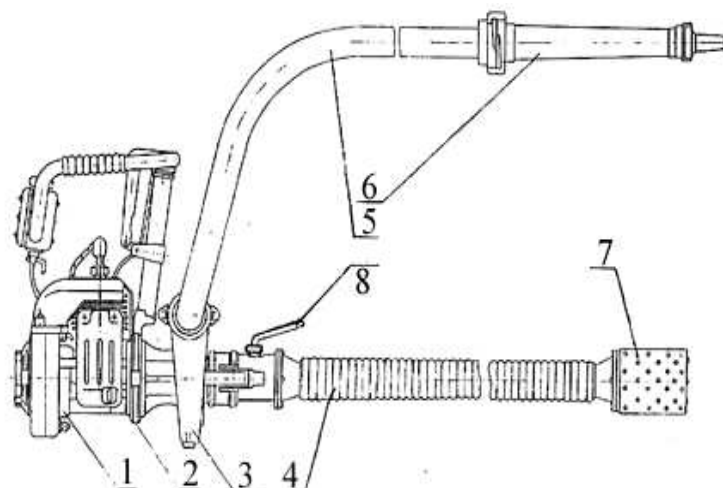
Лесопожарная мотопомпа МЛН-3/0,35У1: 1 – двигатель внутреннего сгорания; 2 – хомут соединительный; 3 – центробежный насос; 4 – всасывающий водозаборный рукав с гибким валом; 5 – пожарный рукав; 6 – пожарный ствол РС-504; 7 – фильтр с осевым лопастным насосом; 8 – ручка-переключатель кулачковой муфты
